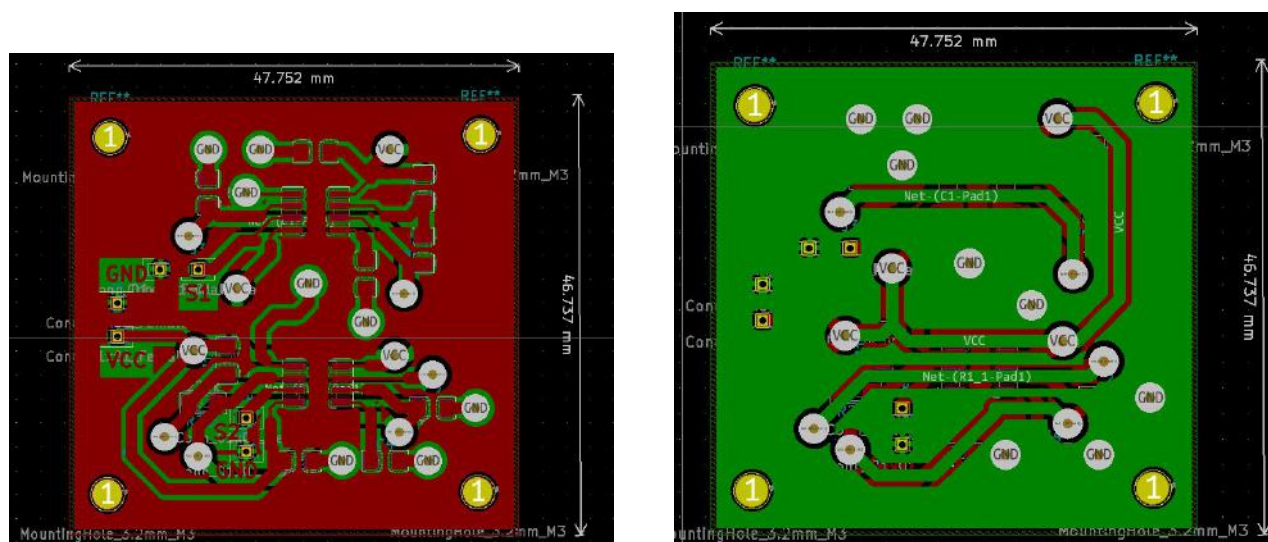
PCB top et bottom de la carte de commande des LEDs sur KiCad
